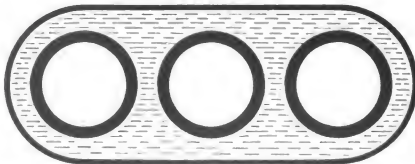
Zylinderblock mit 3 vollständig umspülten Zylindern (Wasser kann zwischen den Zylindern durchtreten).
